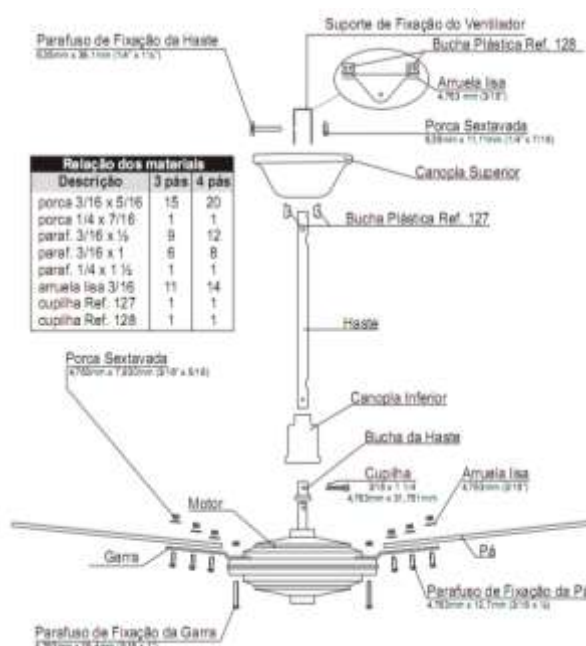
Perspectiva explodida demonstrando os componentes do ventilador A.
